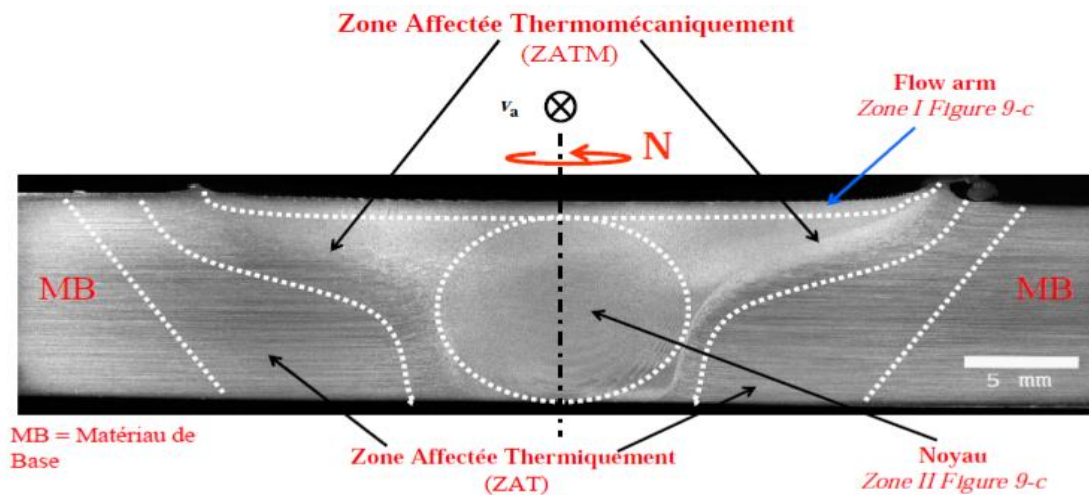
Macrographie d'un cordon de soudure FSW lors du soudage bout à bout de deux plaques d'aluminium [16].
